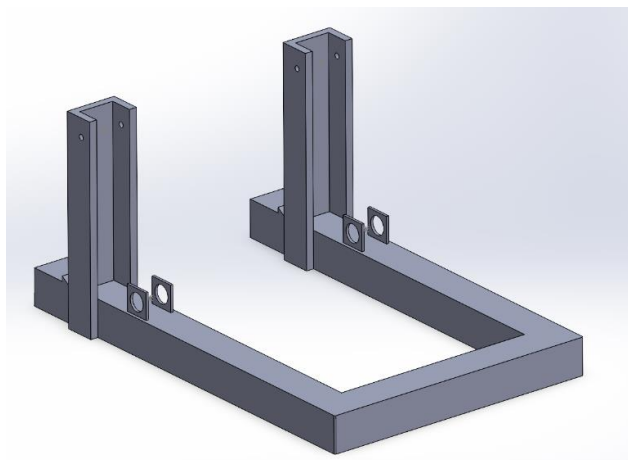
Conjunto bancada, diseñado en SOLIDWORKS
